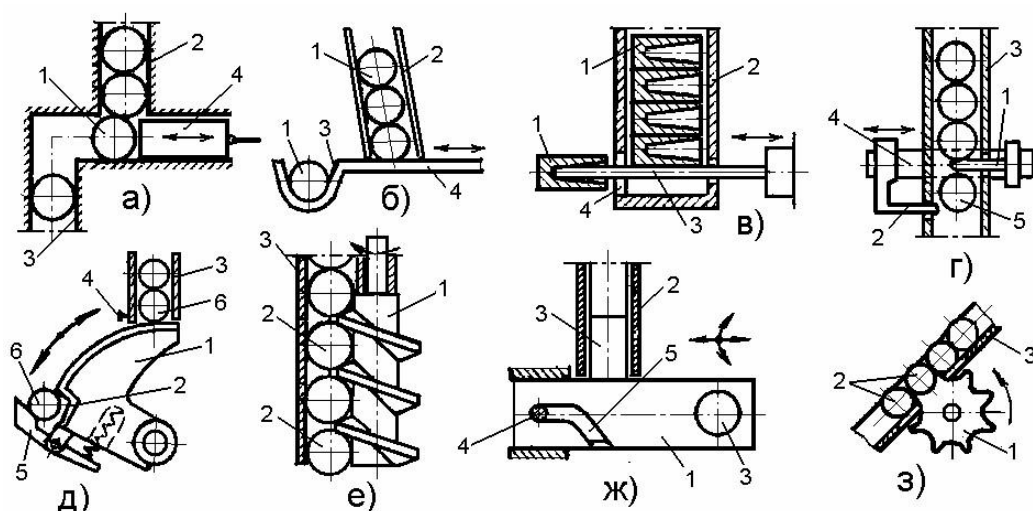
Конструктивные исполнения механизмов выдачи изделий
